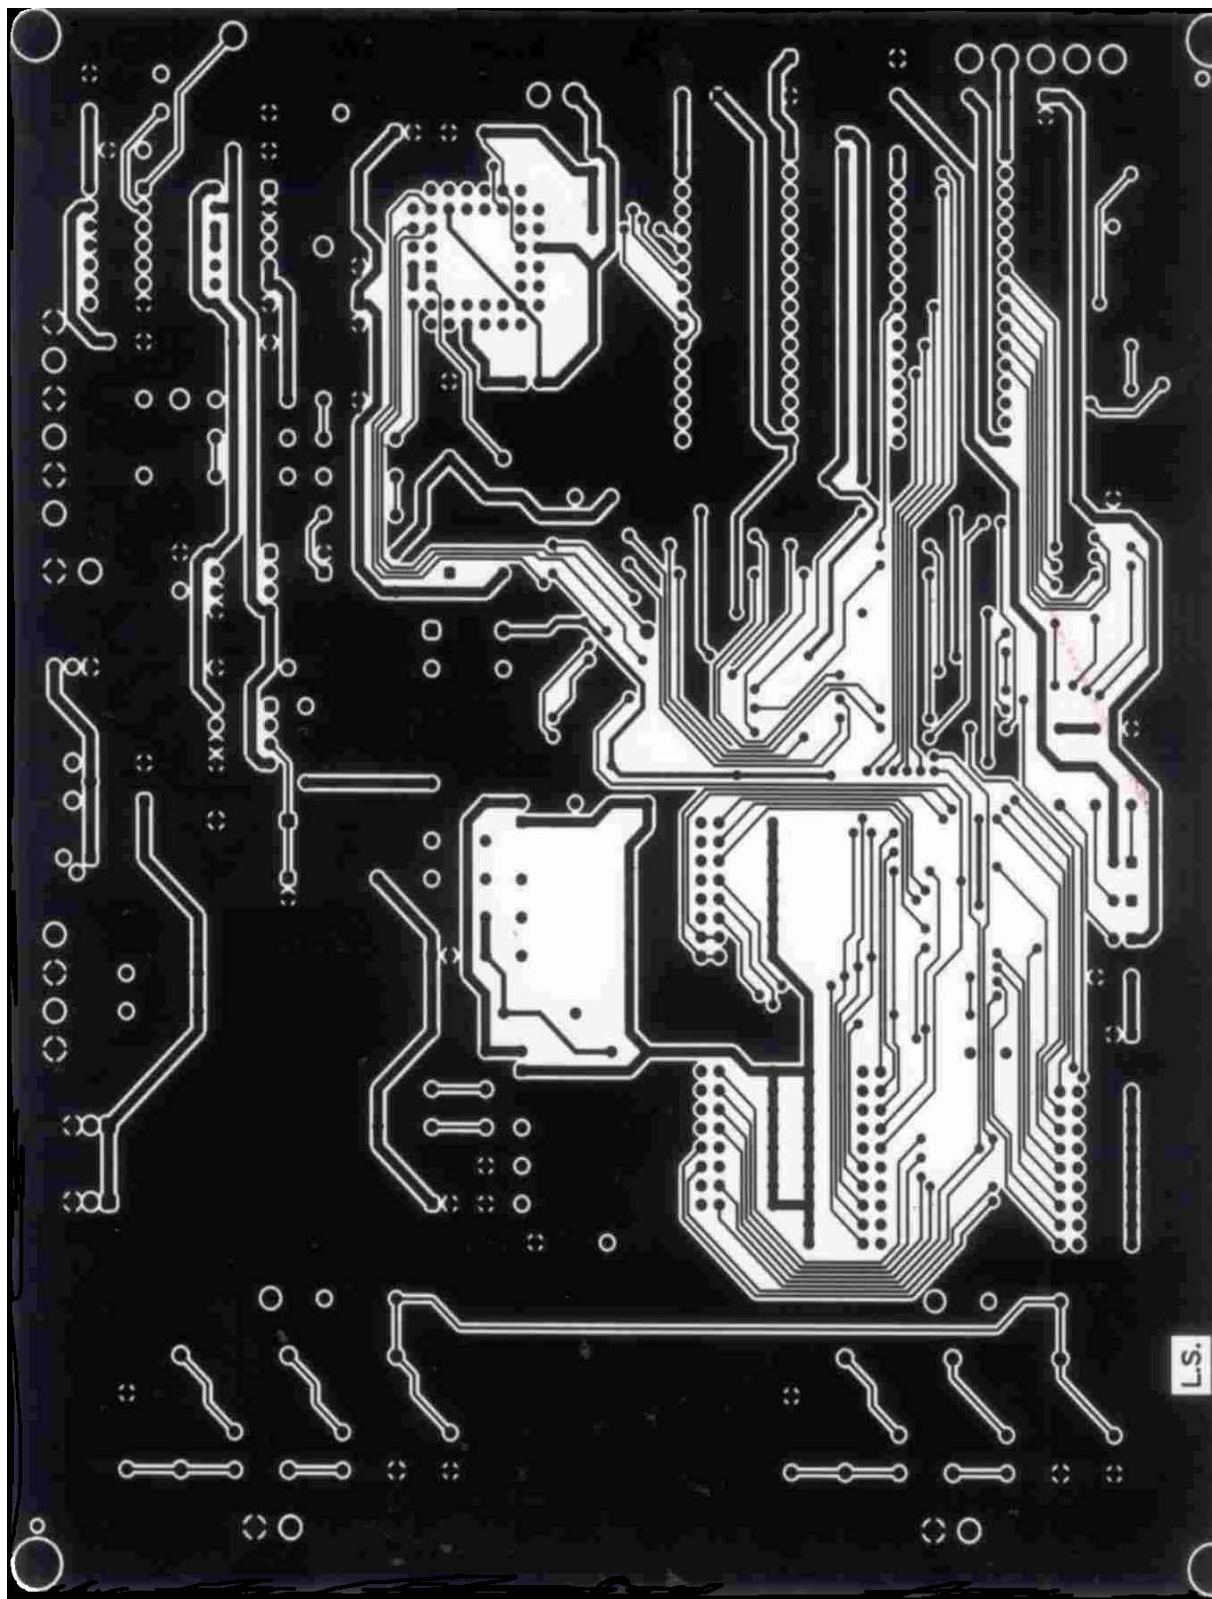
Layout da Placa Impressa do Transmissor/Lado da Solda (L.S.)
